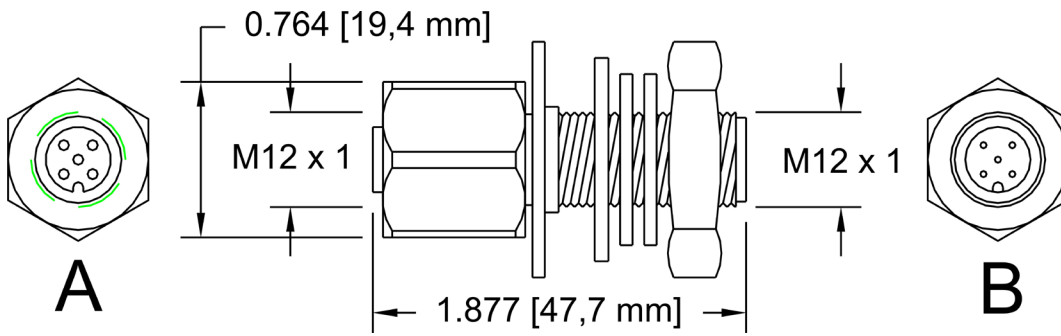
J-LX-B Lynx™ - dessins dimensionnels
